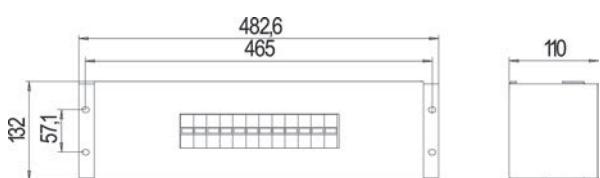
Габаритный чертеж ЩРЗ-6
